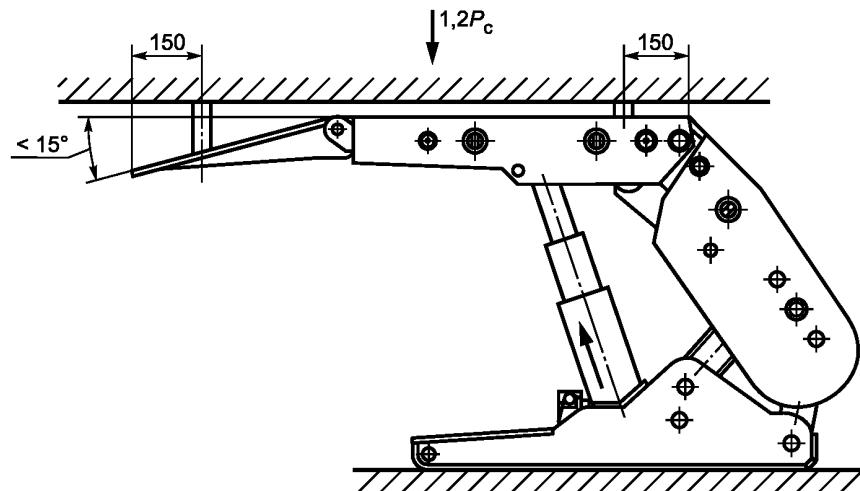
Схема нагружения для определения сопротивления на конце гидроподжимной консоли перекрытия рычажного типа
